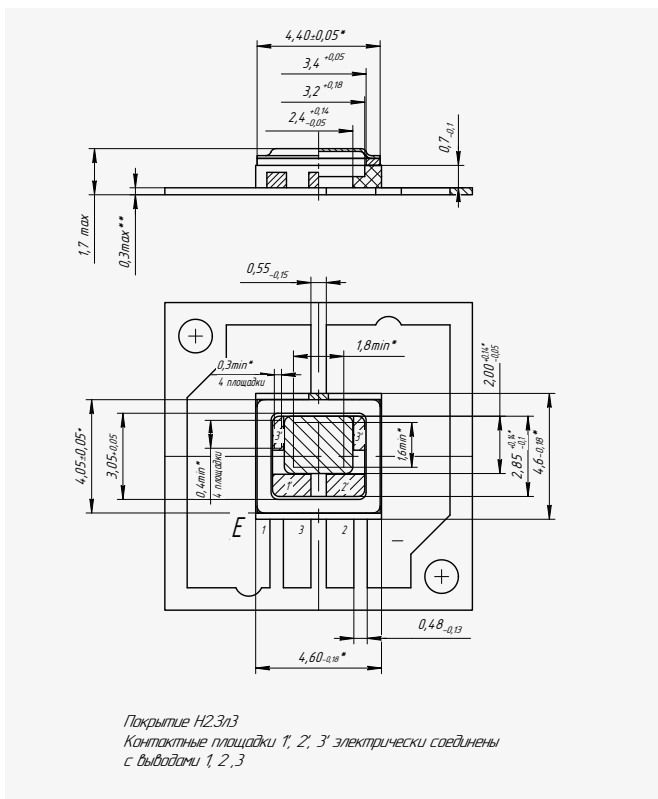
Габаритный чертеж металлокерамического корпуса 5220.3-2.01 K
